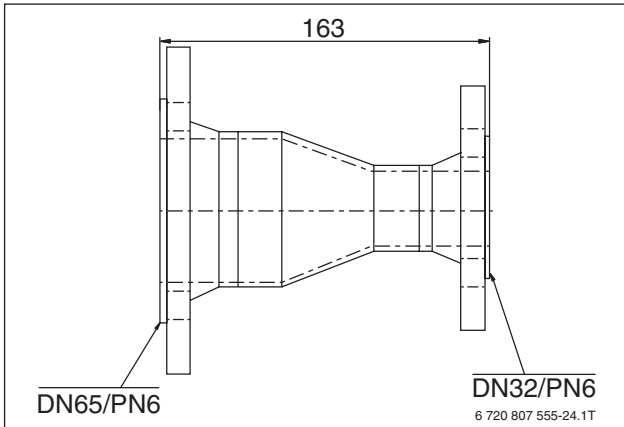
Anschlussstück DN 65/PN 6 – DN 32/PN 6
